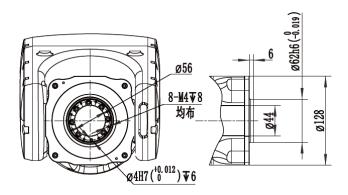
Размеры фланца CRP-RH14-10-W.
